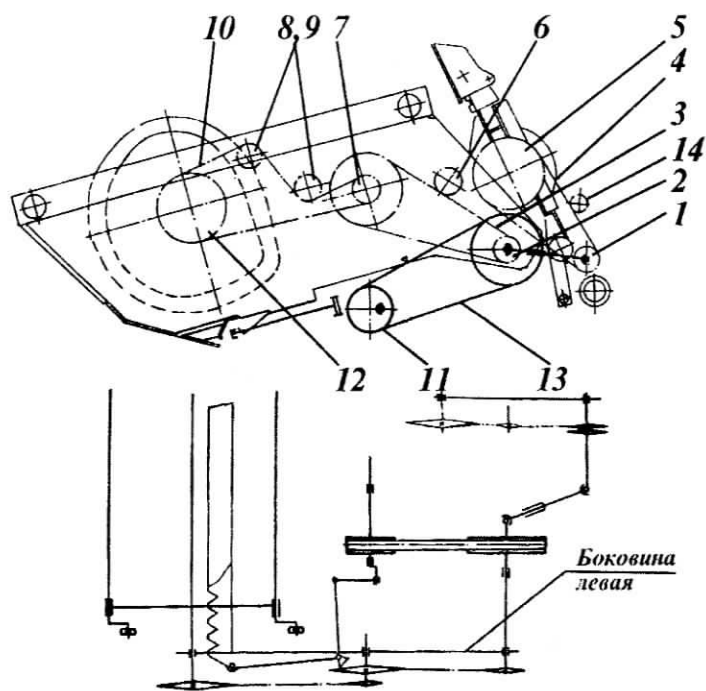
Схема кинематическая жатки для уборки трав (вид слева)
